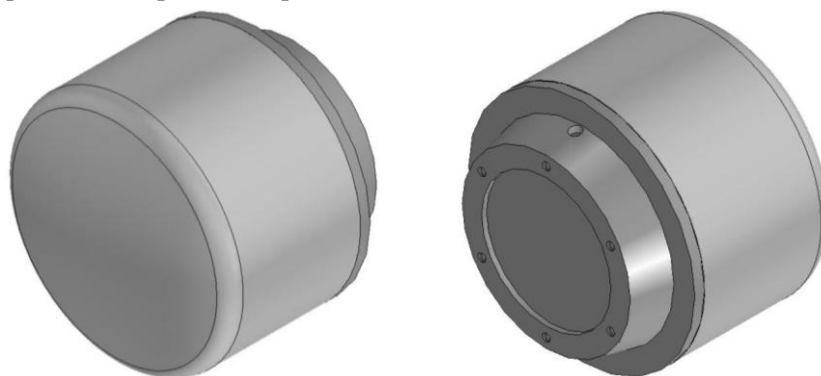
Сборочная трехмерная модель исследуемого двигателя-маховика
